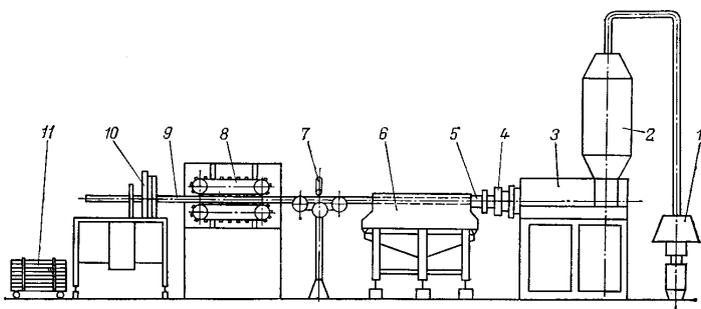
Экструзионный агрегат для изготовления труб:
